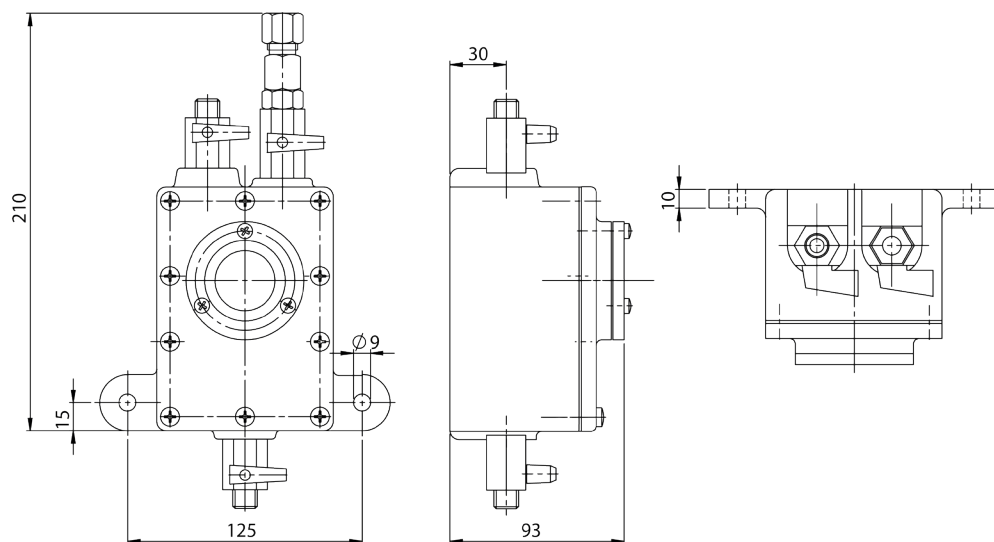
Размерный эскиз газоотборного устройства ZG 1.2.
